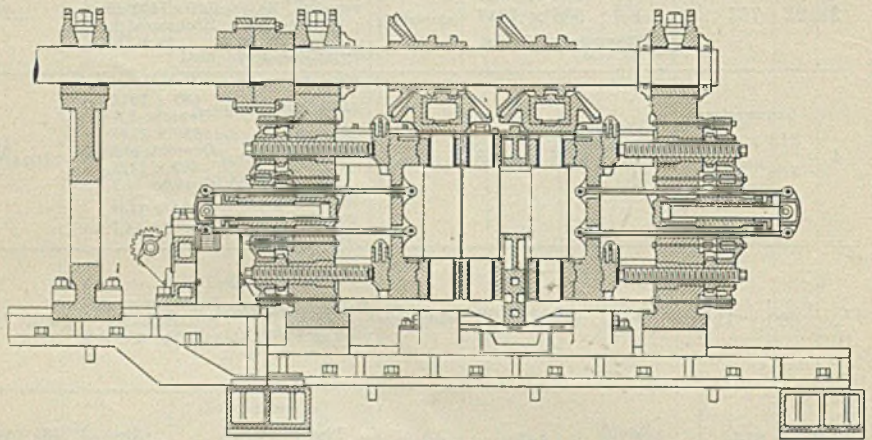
Universalstraße der Lackawanna Steel Co. mit drei Vertikalwalzen.
